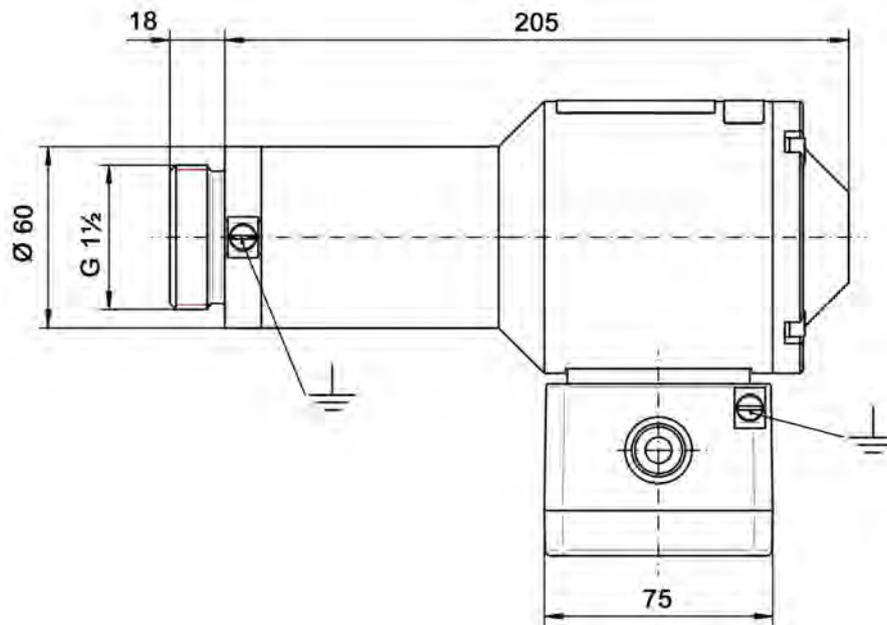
Maßzeichnung Kompaktflammwächter F200K Ex (für Ex-Zone 1, 21), mit Anschlussraum
